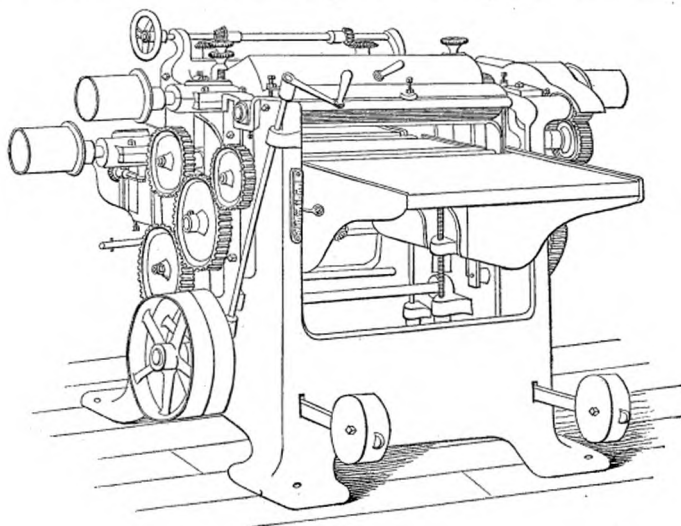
Machine à raboter n° 2 de la Egan Company.
